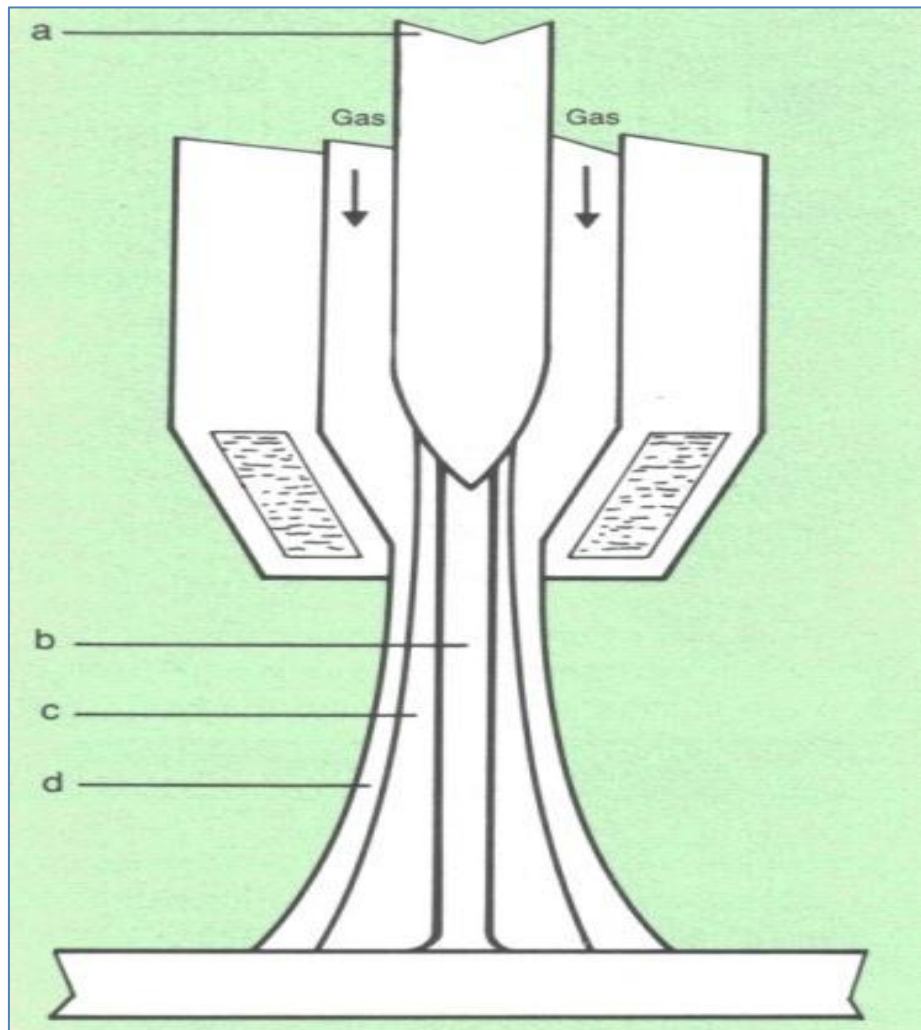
Pistola de corte y soldadura al plasma.
